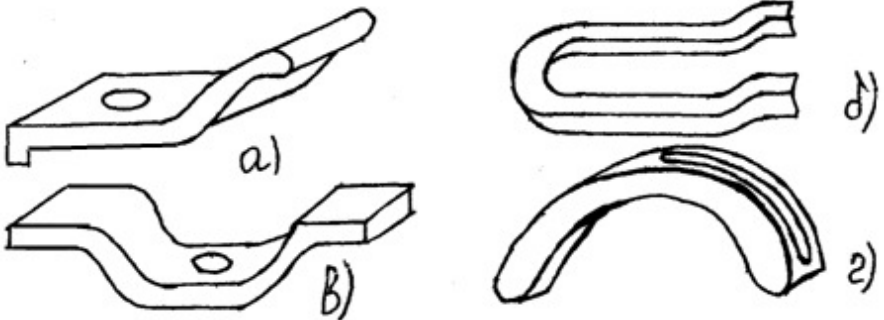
Типи прихватів: а - плиточні; б - вилкоподібні; в - коритоподібні; г - вигнуті універсальні
